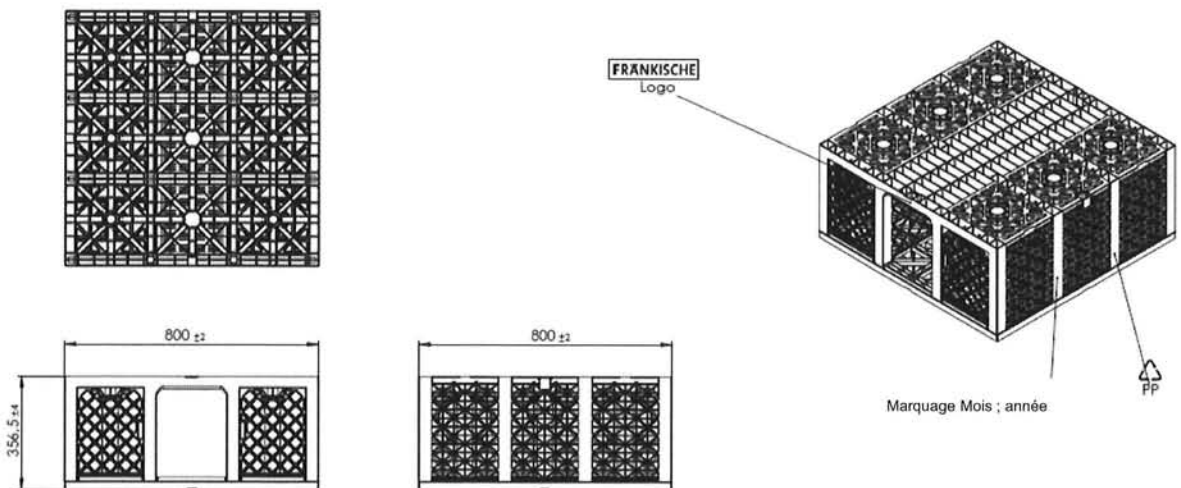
c- Caractéristiques dimensionnelles du demi-module RIGOFILL INSPECT
